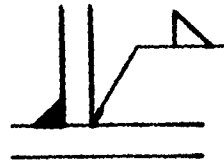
SIMBOLOS UTILIZADOS EN LOS PLANOS DE PROYECTOS DE CONSTRUCCIONES SOLDADAS
